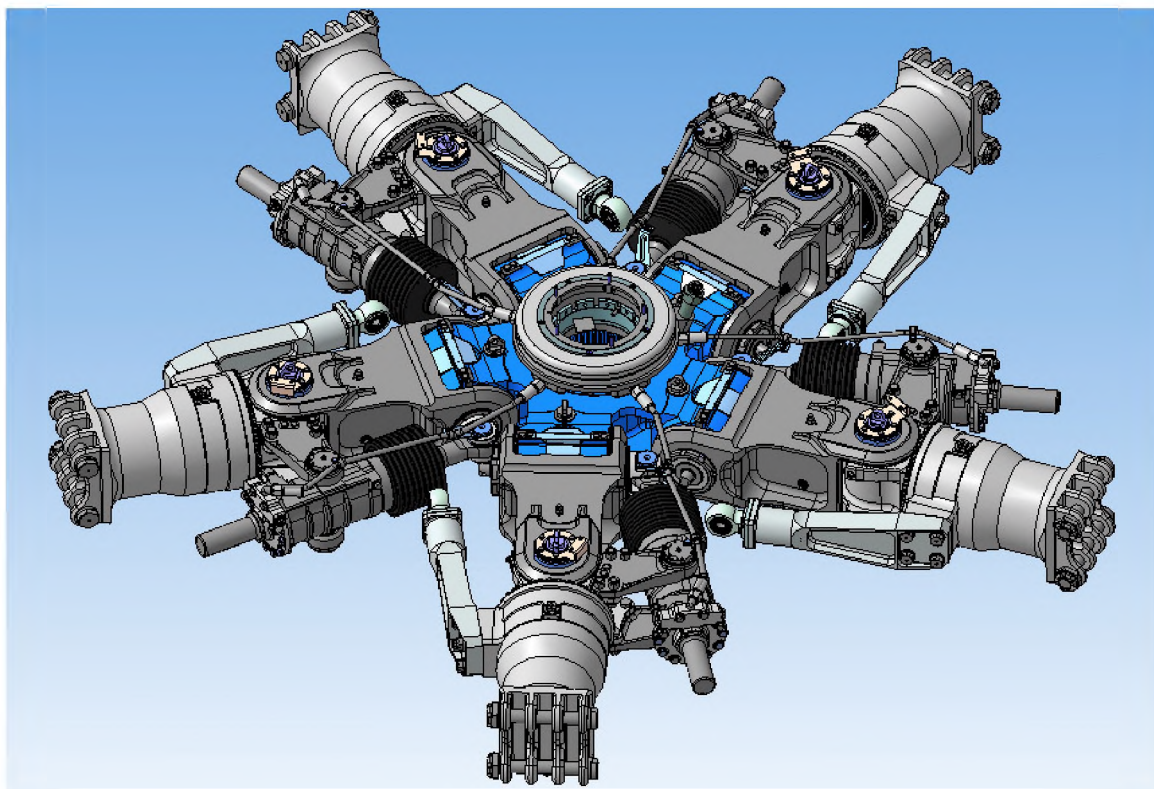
Общий вид шарнирной втулки НВ вертолета Ми-24А:
